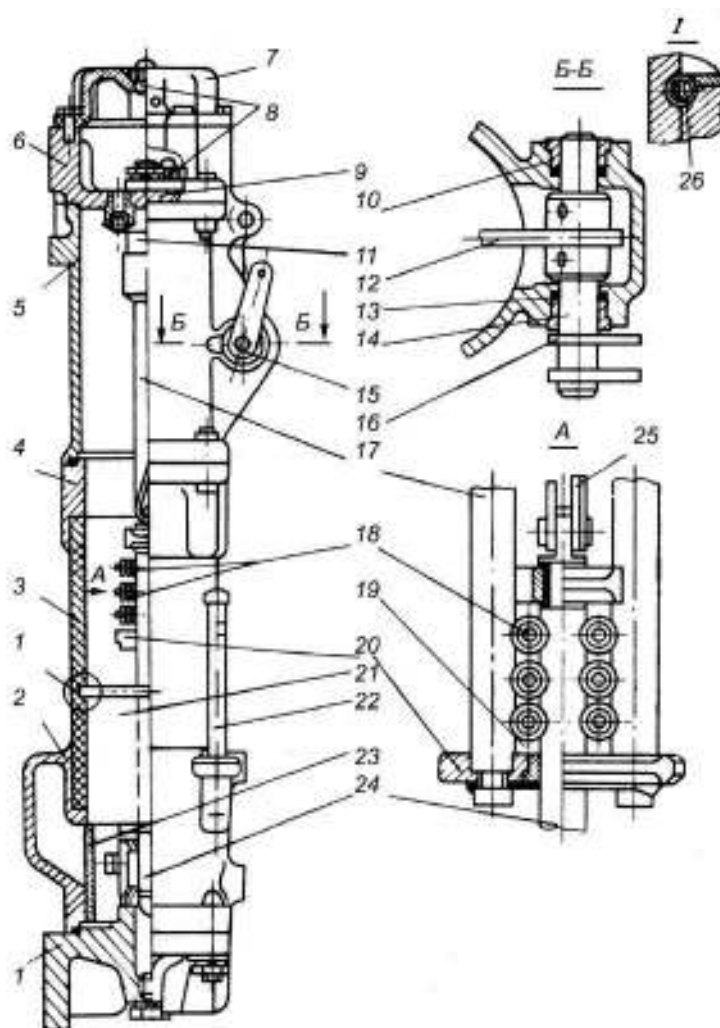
Полюс выключателя ВМПЭ-10 до 1600 А: 1 – крышка нижняя; 2 – фланец нижний; 3 – цилиндр; 4 – фланец верхний; 5 – корпус; 6 – головка; 7 – крышка верхняя; 8 – пробка маслоспускowego устройства; 9 – клапан; 10 – подшипник; 11 – буфер; 12 – рычаг механизма отверстия; 13 –
